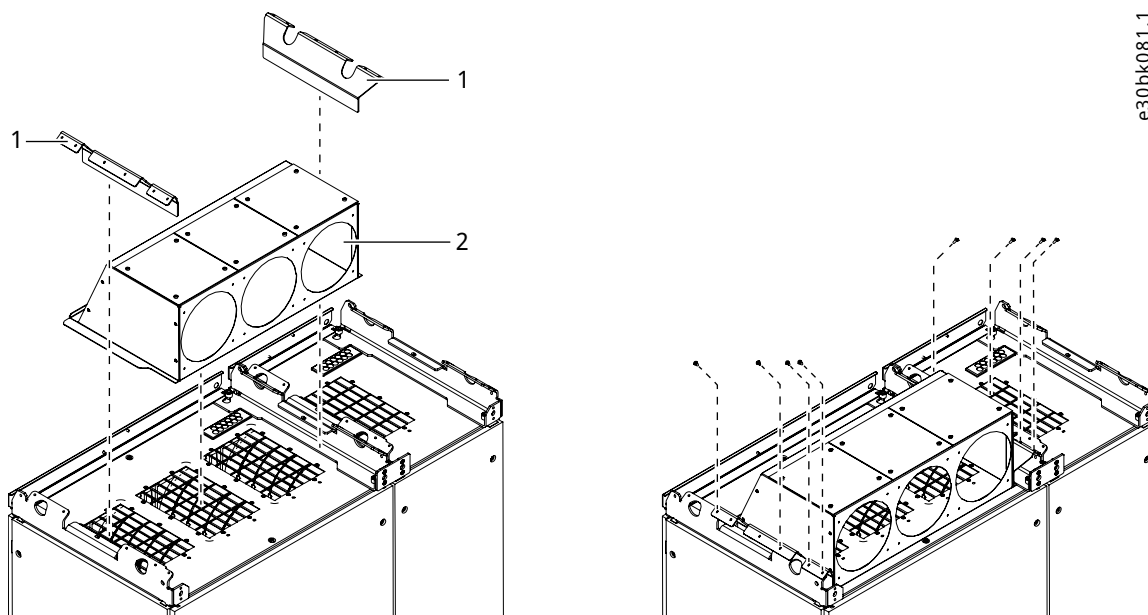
Installation de la plaque de protection de l'option de refroidissement par canal arrière
